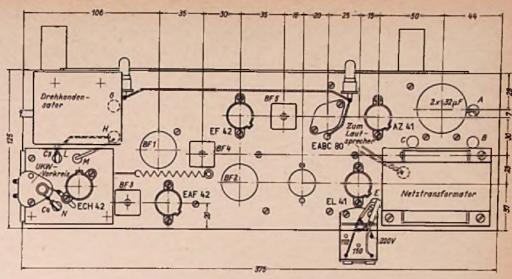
Draufsicht auf das Chassis mit der Verteilung der Haupt-Einzelteile
